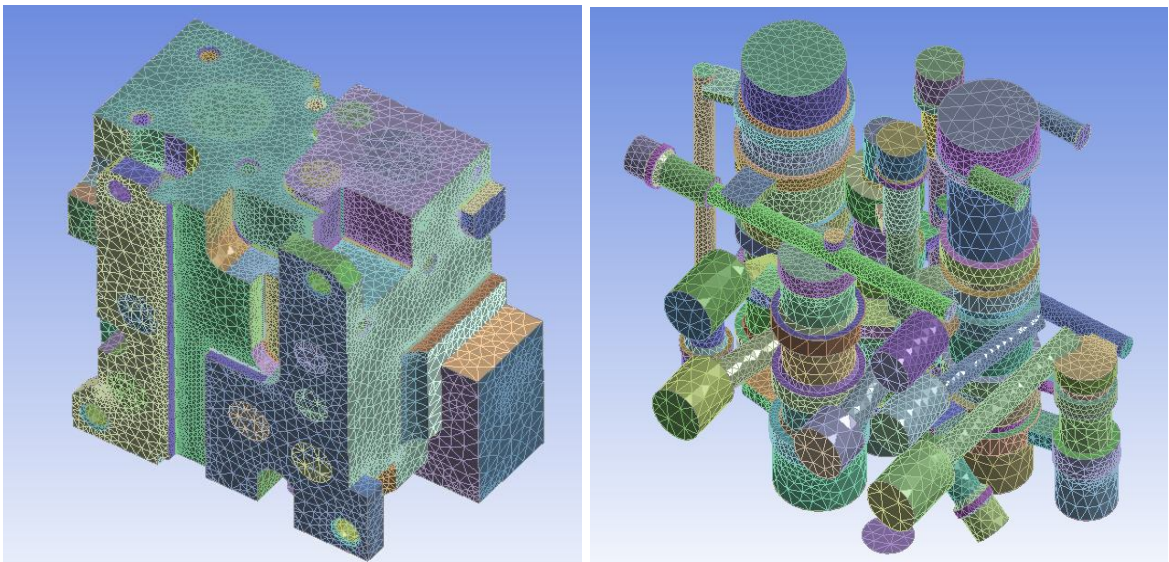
Твердотіла модель корпусу агрегату двигуна ЛА
